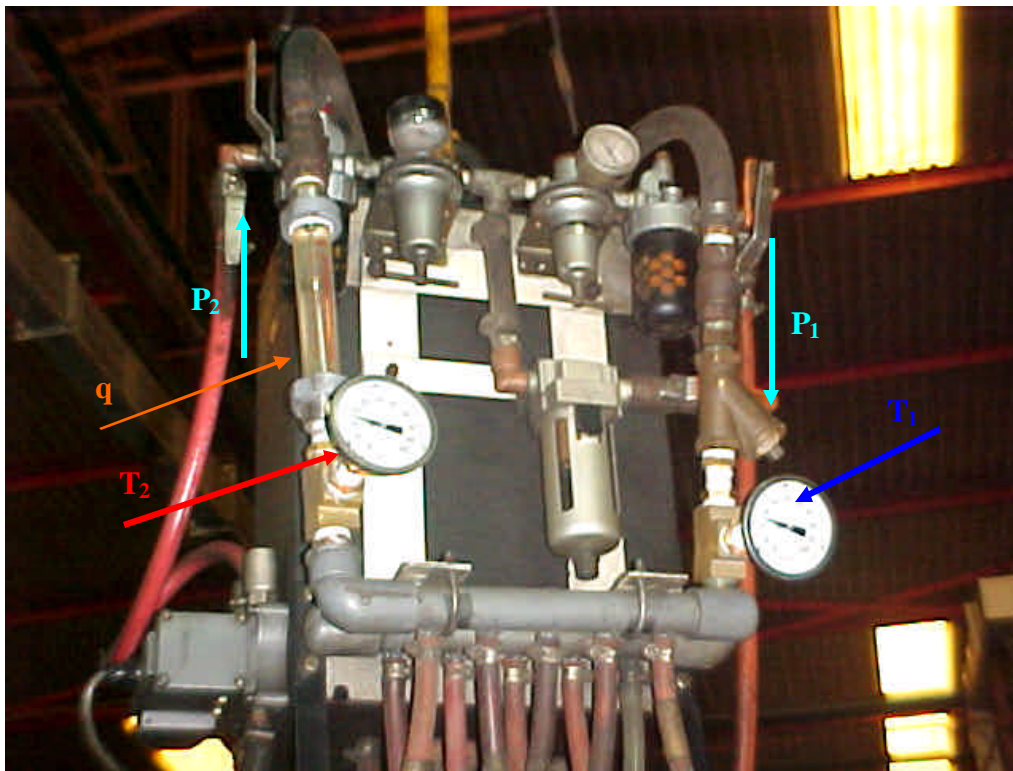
Instrumentación utilizada en equipos de soldadura
